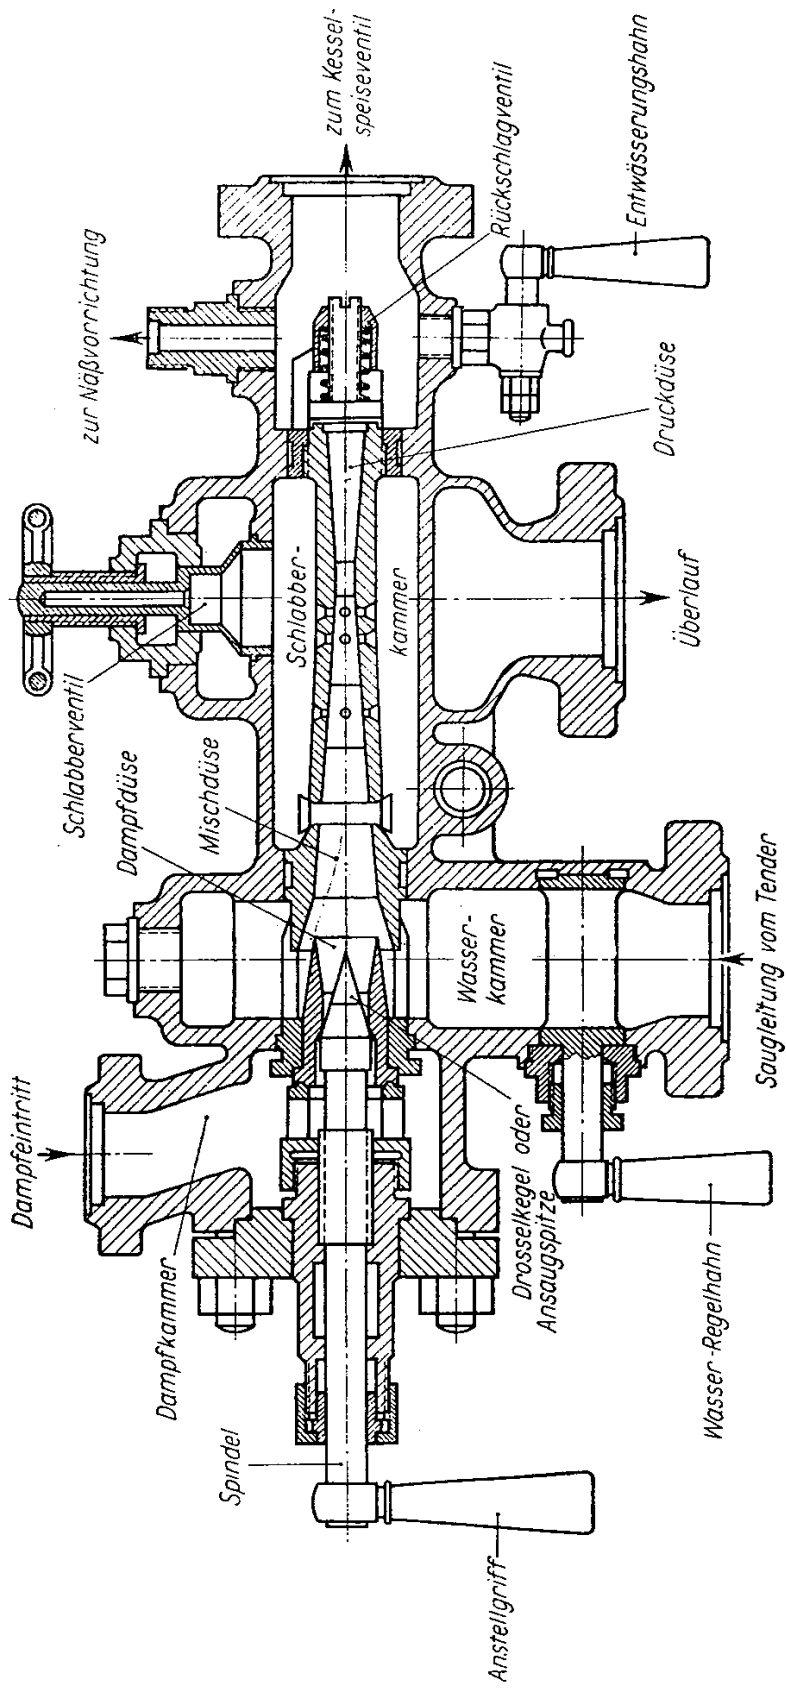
Dampfstrahlpumpe -ältere Bauart-
